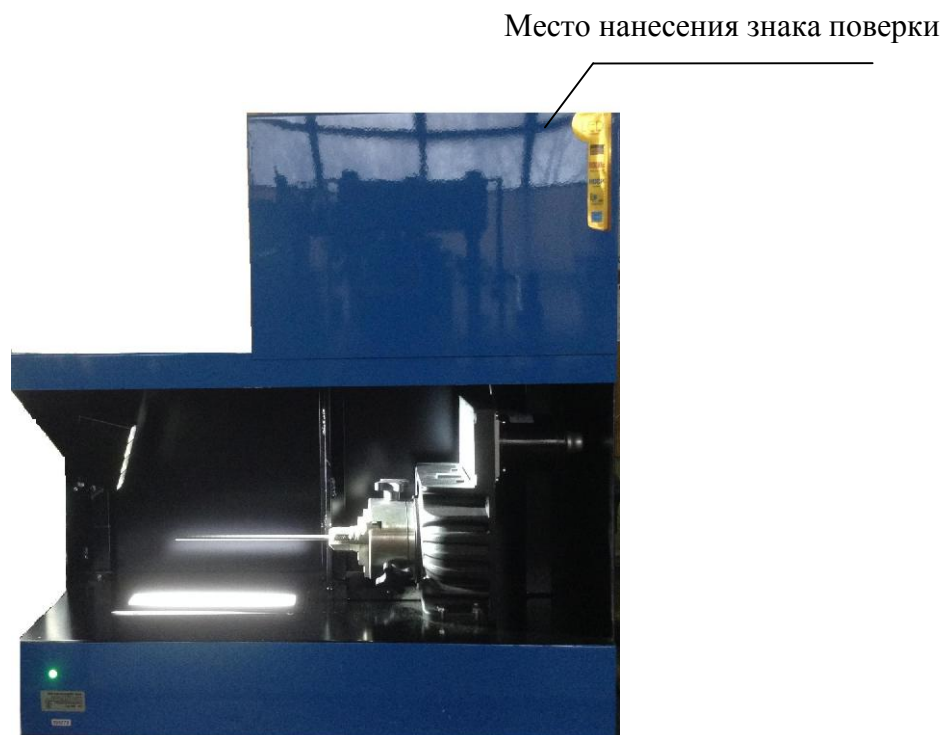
Общий вид прибора и обозначение места нанесения знака поверки
